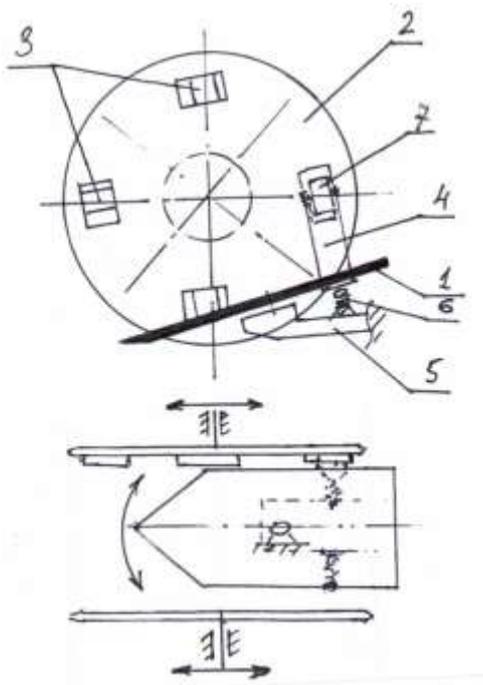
Схема предлагаемой конструкции подкапывающего органа.
